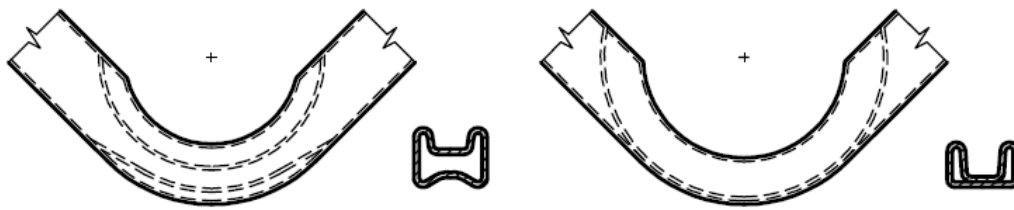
Změny průřezu profilu [14], [31], [46]
